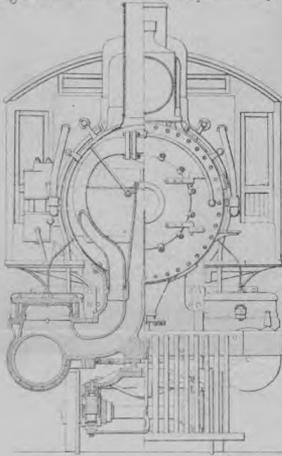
Elevation d'avant et Coupe sur les Cylindres.
